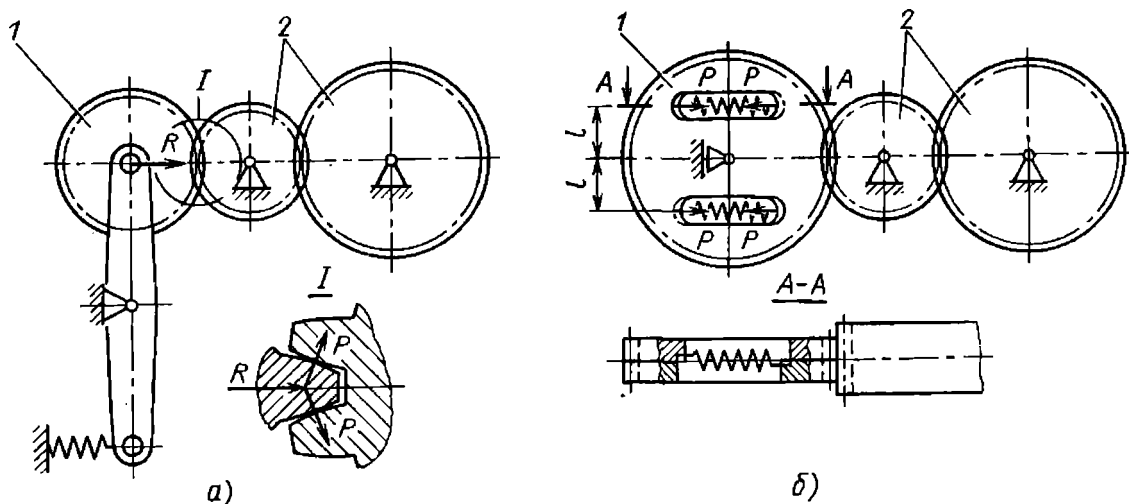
Ротапринтный метод смазывания зубчатых колес:
